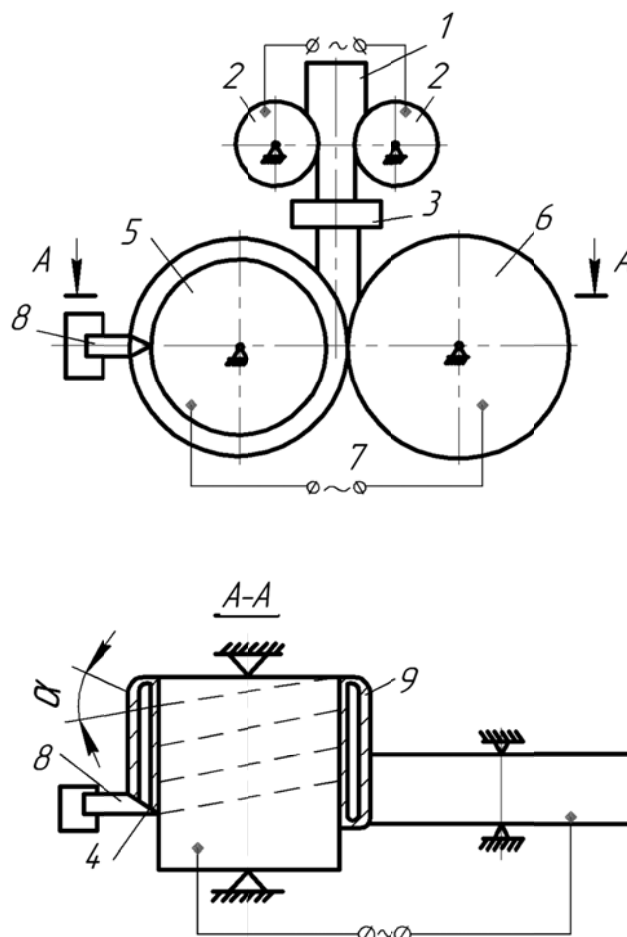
Схема электроконтактной наплавки порошка в металлической оболочке с обрезкой кромок и оплавлением оболочки.
